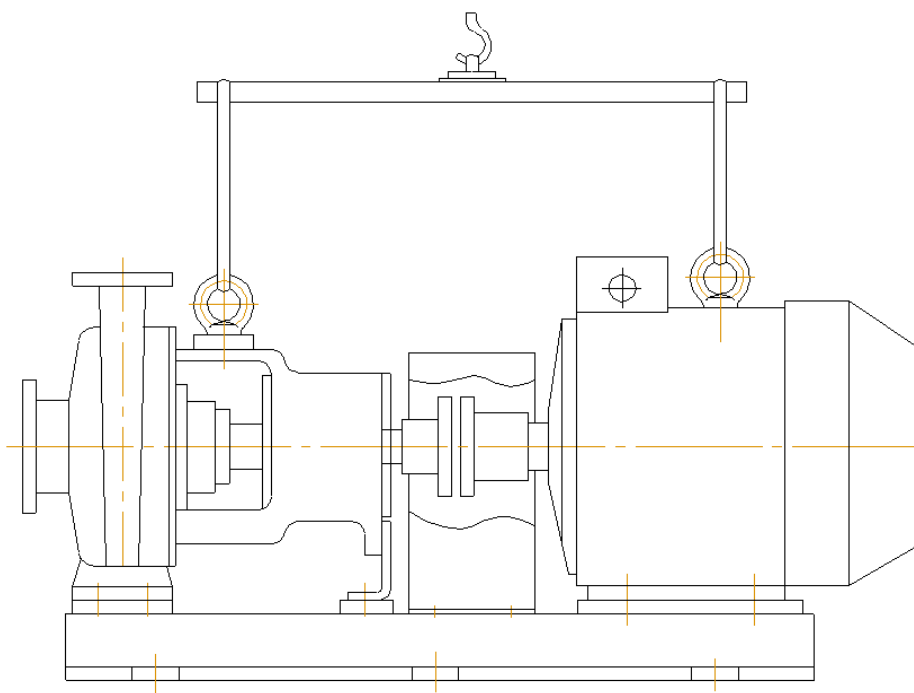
Строповка агрегатов типа «X» и «XO».
